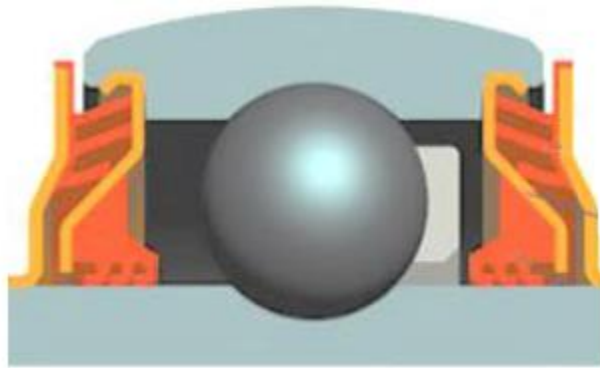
Конструкція системи ущільнювача X-SHIELD-6 підшипника HARP AGRO
